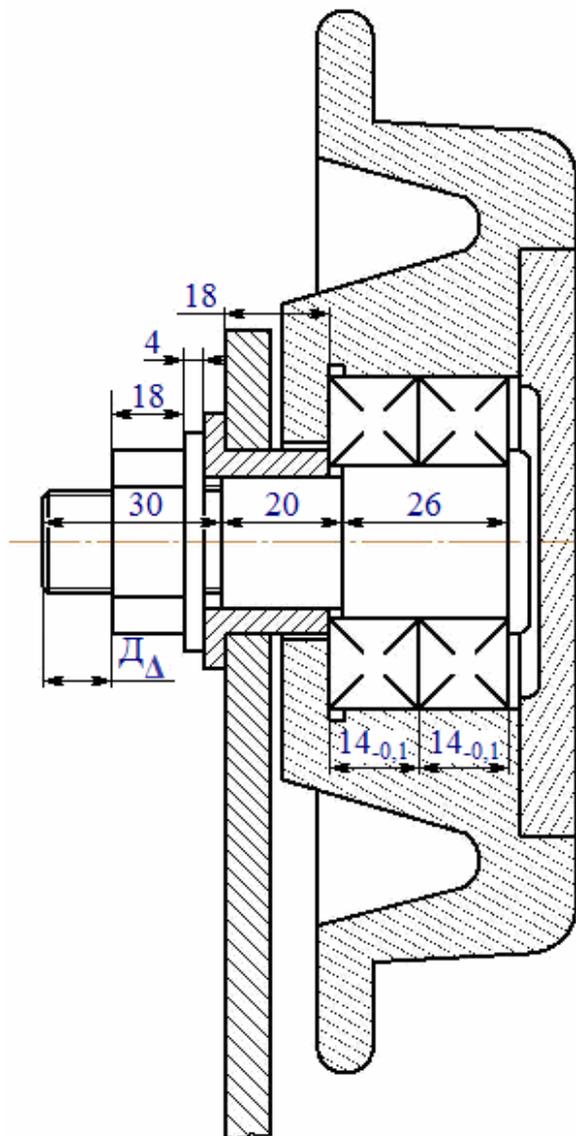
Рабочий чертеж сборочной единицы (цепь  $D$ )
